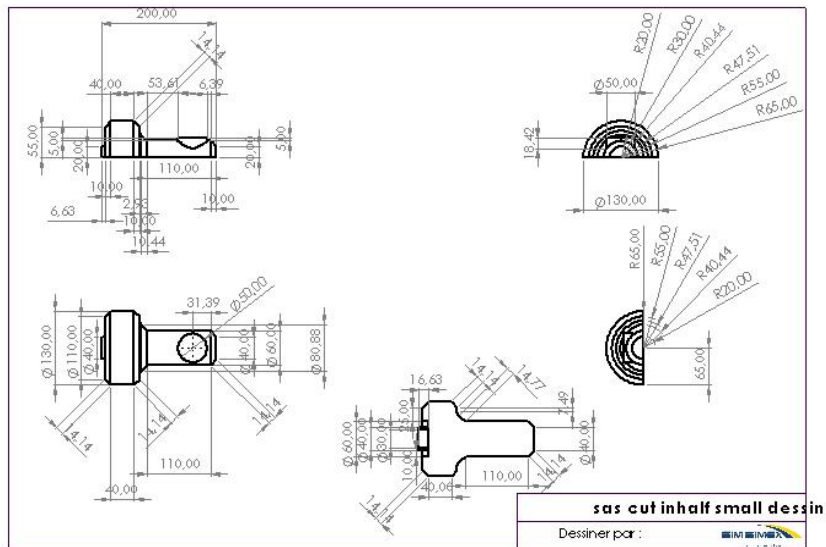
Dessin technique de prototype de SAS Quest sur solidworks
